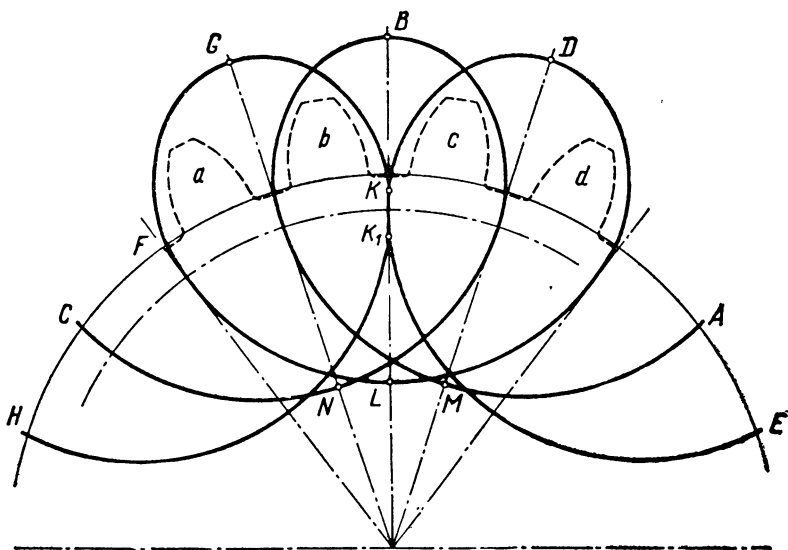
Торцевые фасонные фрезы для образования скосов на зубьях зубчатых колес.
